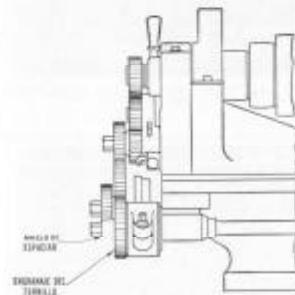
A. Posición del anillo de espaciar para engranajes simples
